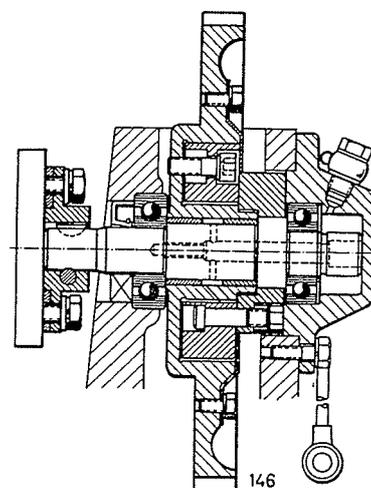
Schmierölaufuhr des Einspritzpumpenantriebes mit Spritzversteller F 6-12 L 614
